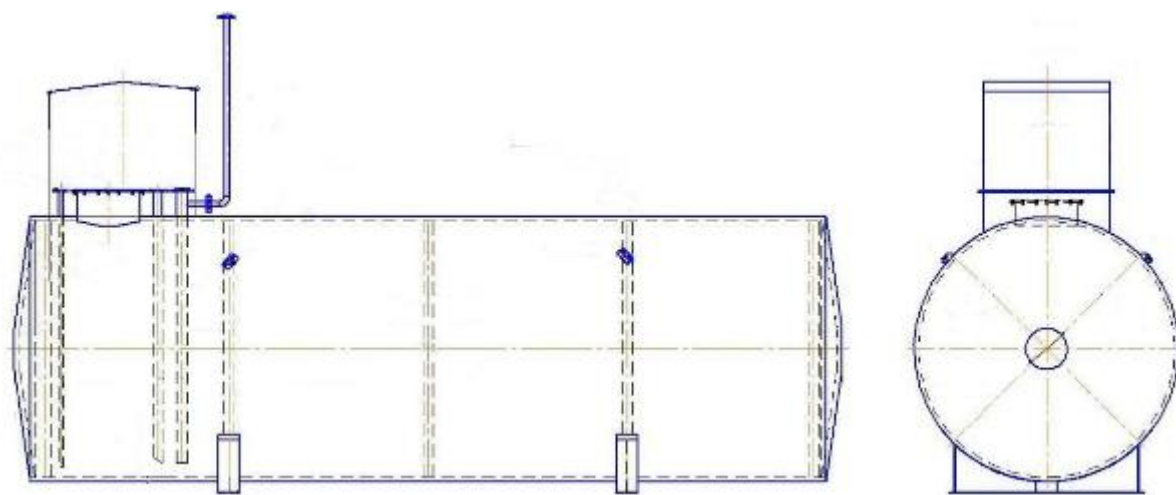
Эскиз общего вида резервуара РГС-25 зав.№ 4
